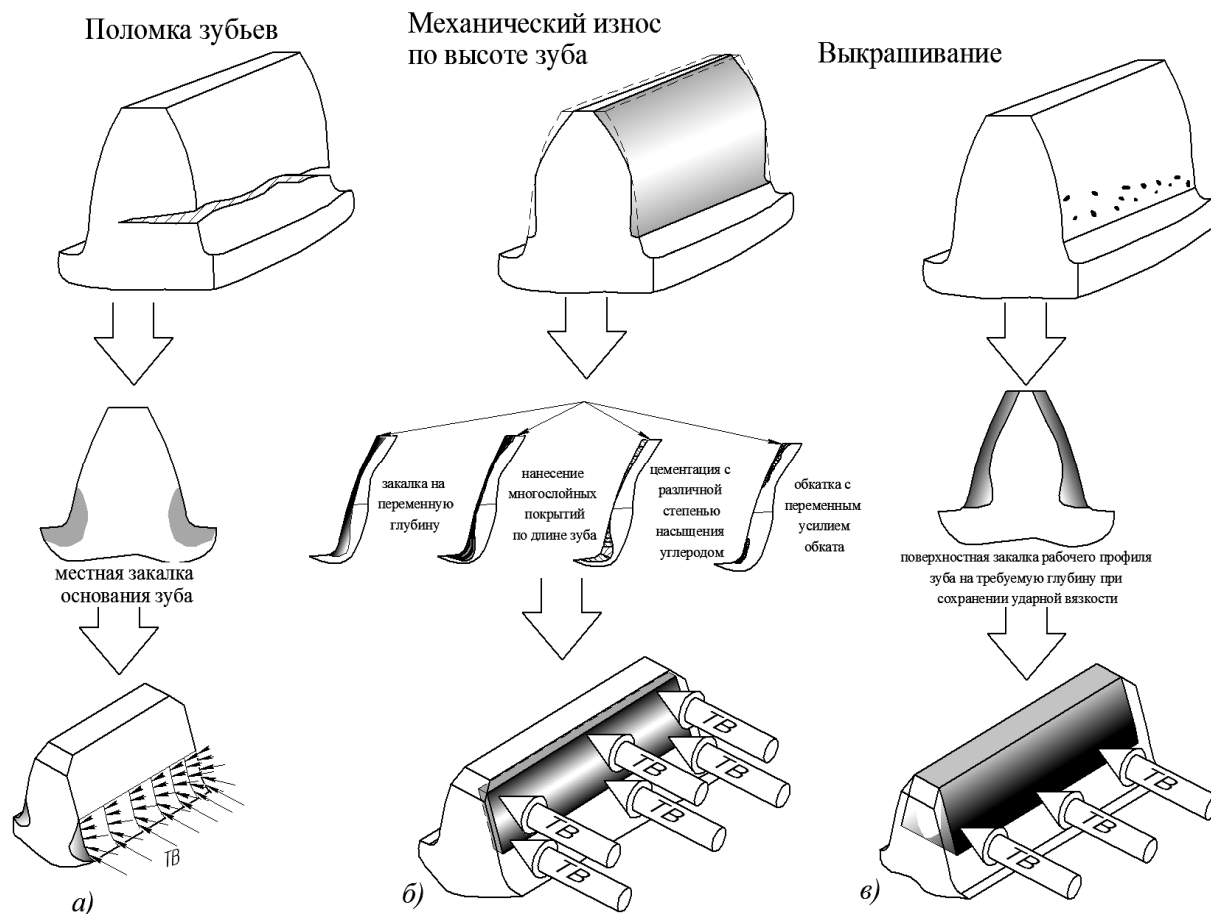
Виды разрушения зубчатых колес: а) поломка зубьев; б) механический износ рабочей поверхности; в) усталостное выкрашивание
